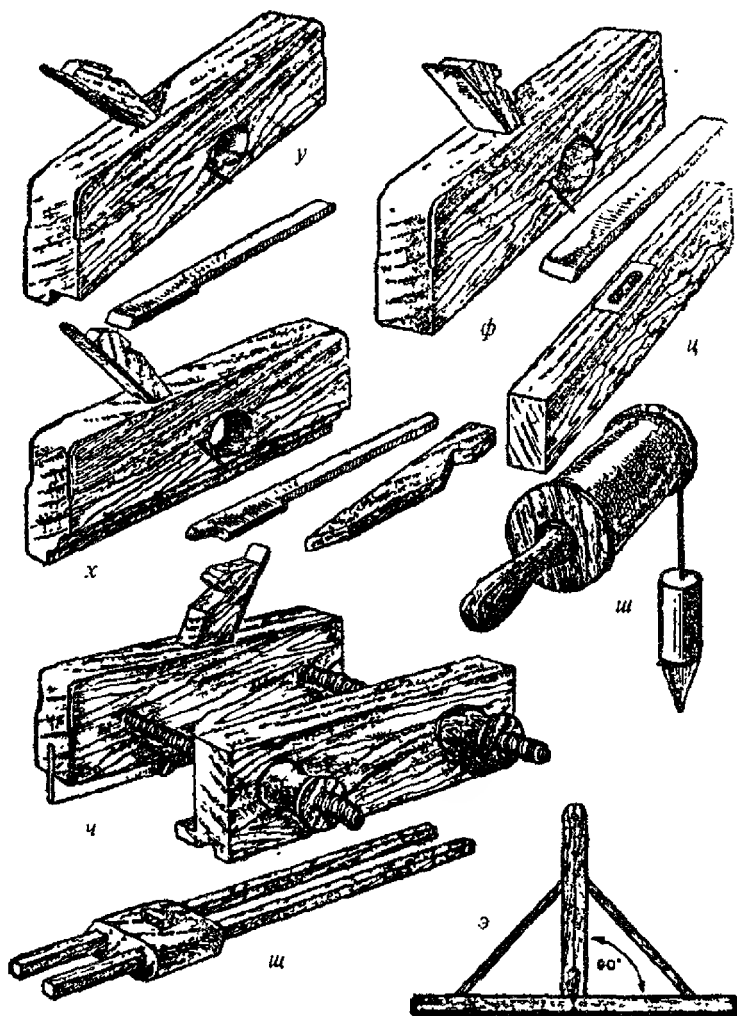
(2). Инструменты и приспособления для обработки дерева
